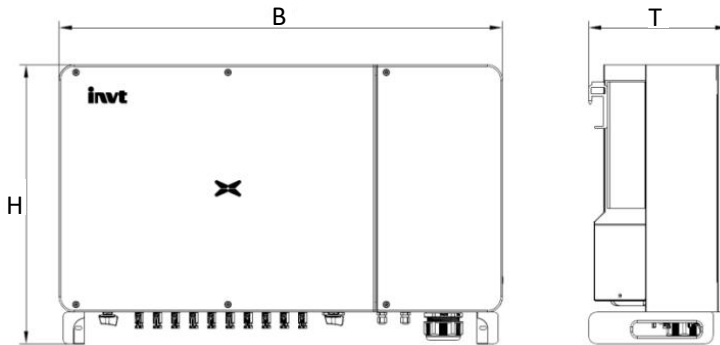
Abmessungen und Gewichte der Wechselrichter
